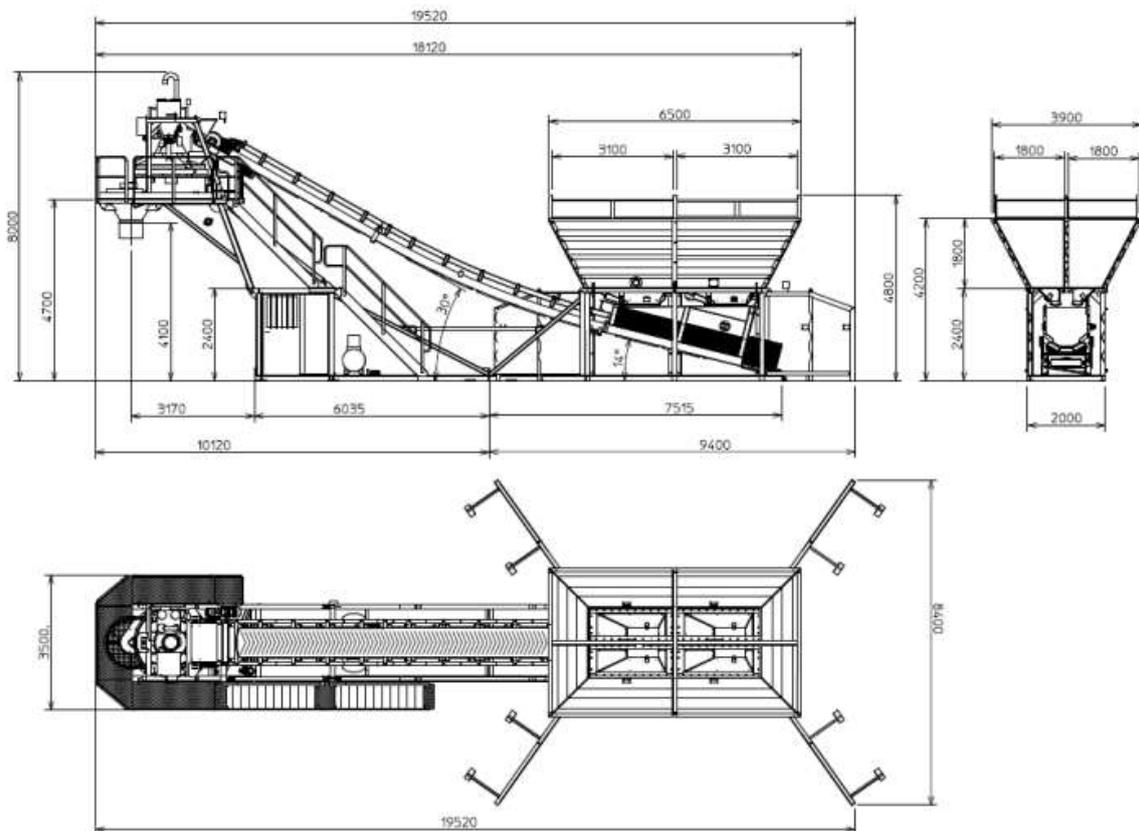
Planta Dosificadora De Concreto Premezclado CIFAMOOVE 30
